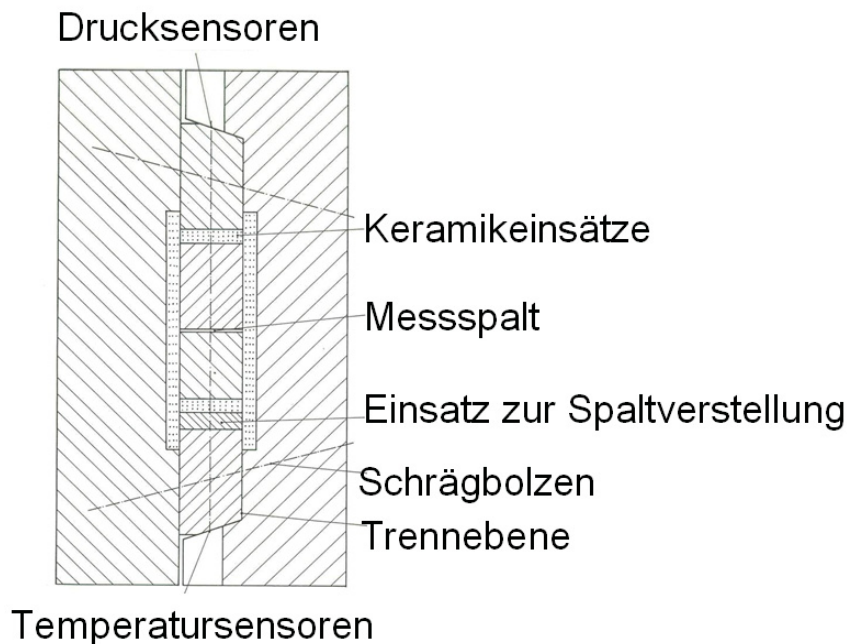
Skizze des Rheometerwerkzeuges von oben [1]
